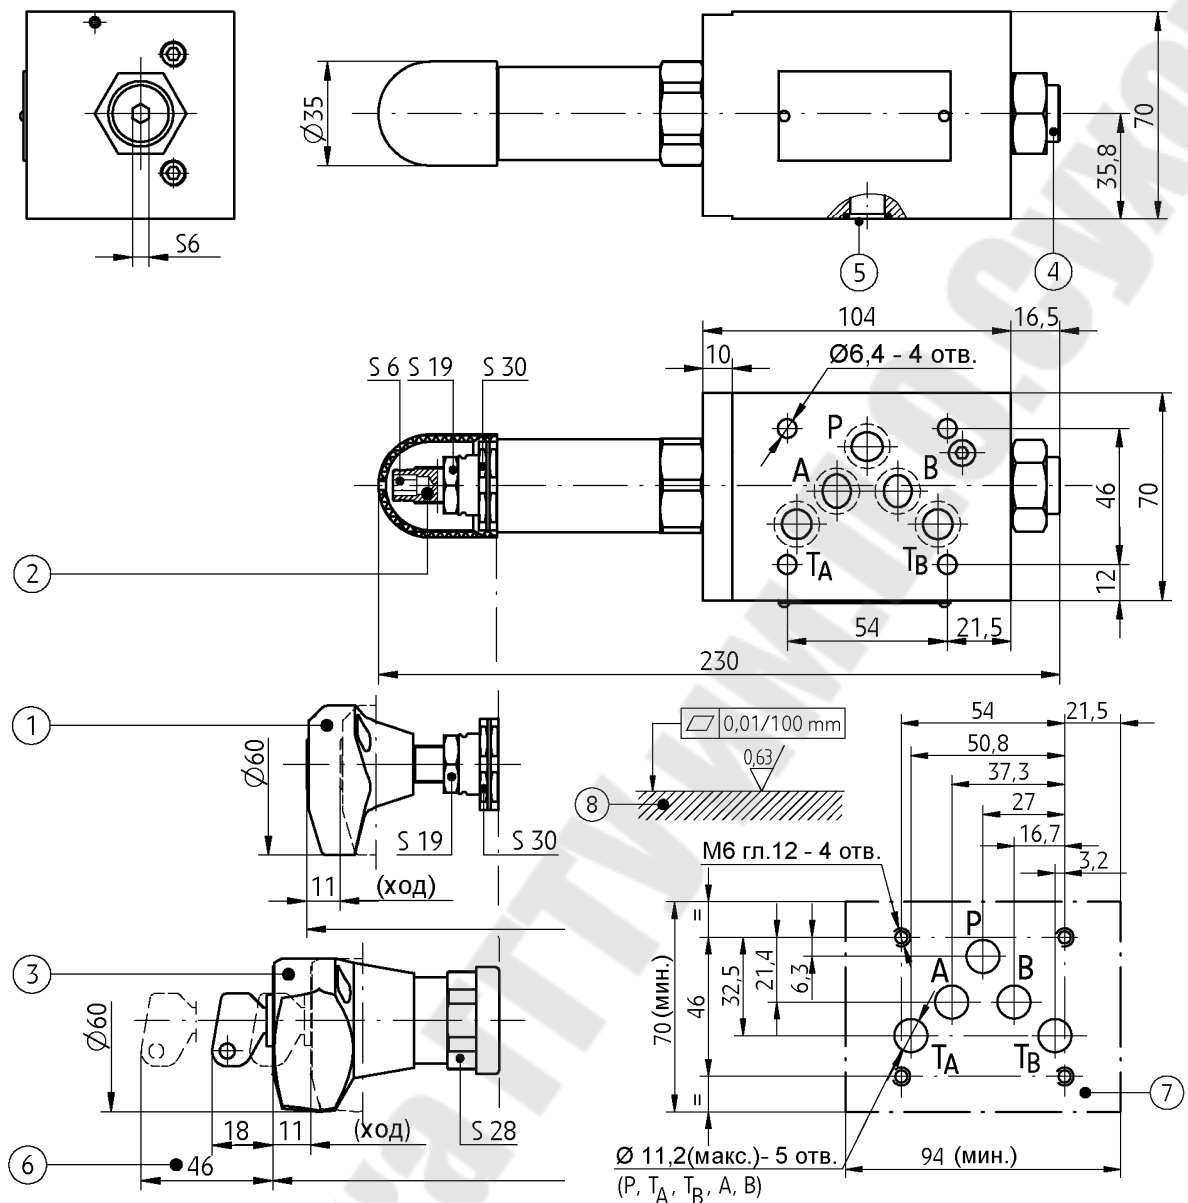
Общий вид габаритные и присоединительные размеры редукционного клапана модульного монтажа непосредственного управления типа UZRC10/22-210-Y-1
